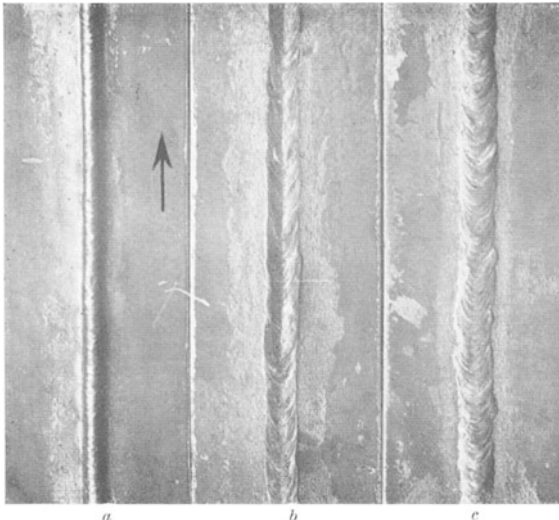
Normale Schweißnähte an 1 mm-Stahlblechen.
